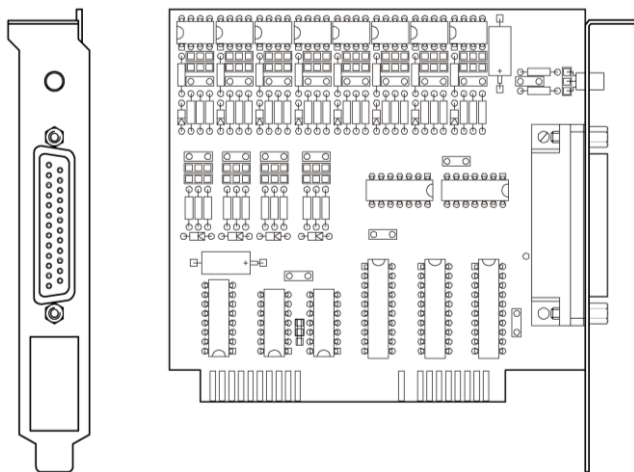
Внешний вид платы сопряжения Ц-32
